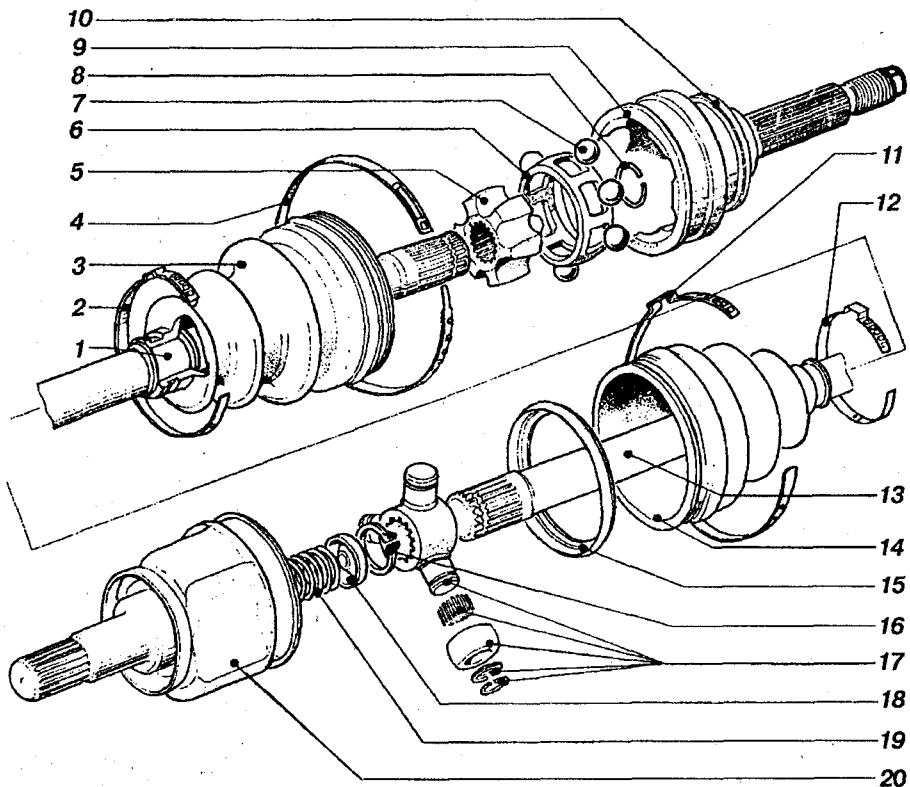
Детали шарнирных валов: 1 – дренажная втулка; 2 – короткий хомут наружного шарнира; 3 – защитный чехол наружного шарнира; 4 – длинный хомут наружного шарнира; 5 – обойма; 6 – сепаратор наружного шарнира; 7 – шарик; 8 – стопорное кольцо; 9 – корпус наружного шарнира; 10 – грязеотражатель наружного шарнира; 11 – длинный хомут внутреннего шарнира; 12 – короткий хомут внутреннего шарнира; 13 – вал шарнирный левый (правый); 14 – защитный чехол внутреннего шарнира; 15 – шайба; 16 – стопорное кольцо; 17 – трёхшиповик внутреннего шарнира в сборе; 18 – чашка пружины; 19 – компенсационная пружина; 20 – корпус внутреннего шарнира в сборе
